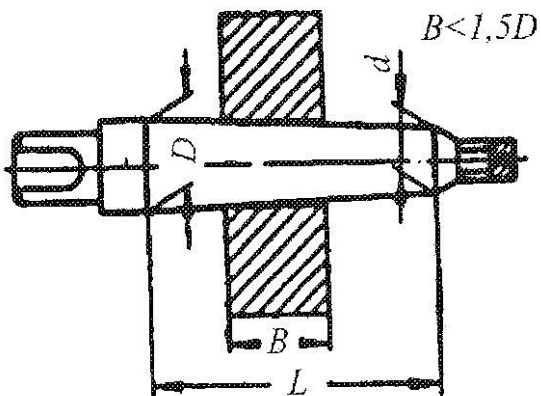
Установа заготовок на жорсткій конічній оправці
